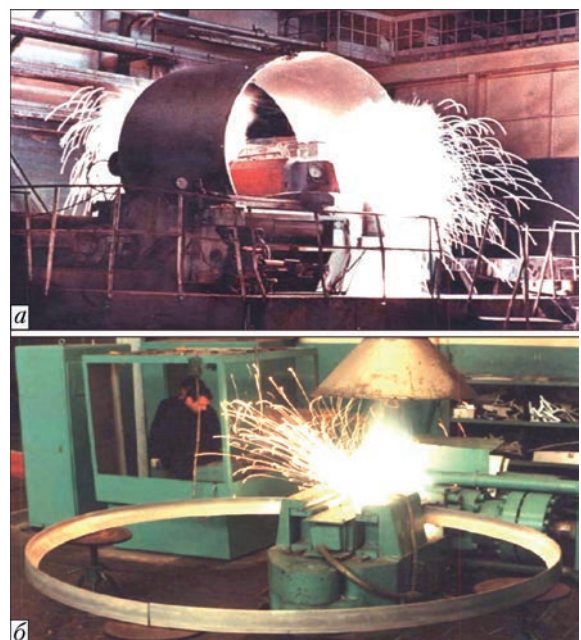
Приклади використання контактно-стикового зварювання у виробництві фрагментів конструкцій аерокосмічної техніки з високоміцного сплаву АМгб: а – зварювання обичайки корпусу паливного баку; б – зварювання шпангоутів
